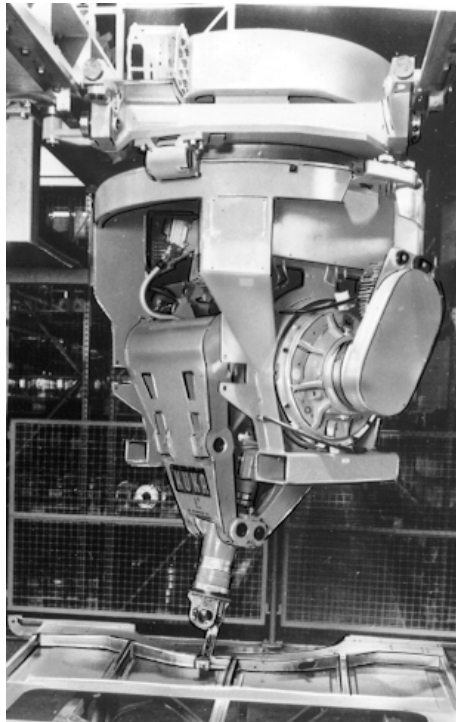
Сварочный робот фирмы КУКА.
